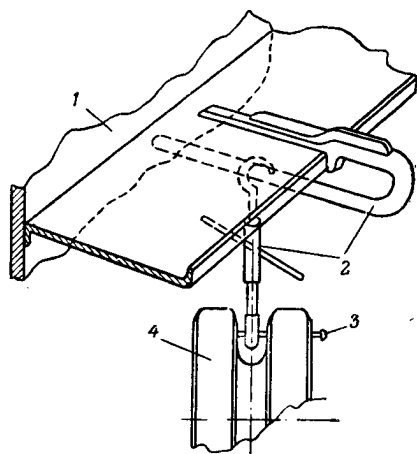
Приспособления для снятия опорного катка: 1 — борт танка; 2 — приспособление; 3 — палец трака; 4 — каток.
